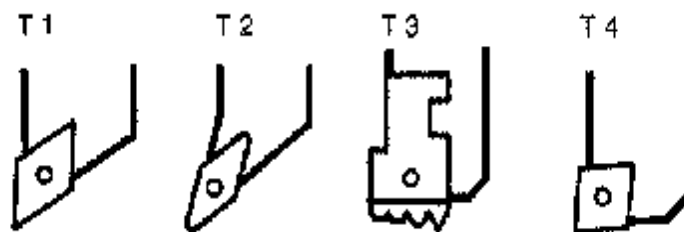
Herramientas de torneado: para desbaste, de acabado, para roscar, de acabado
